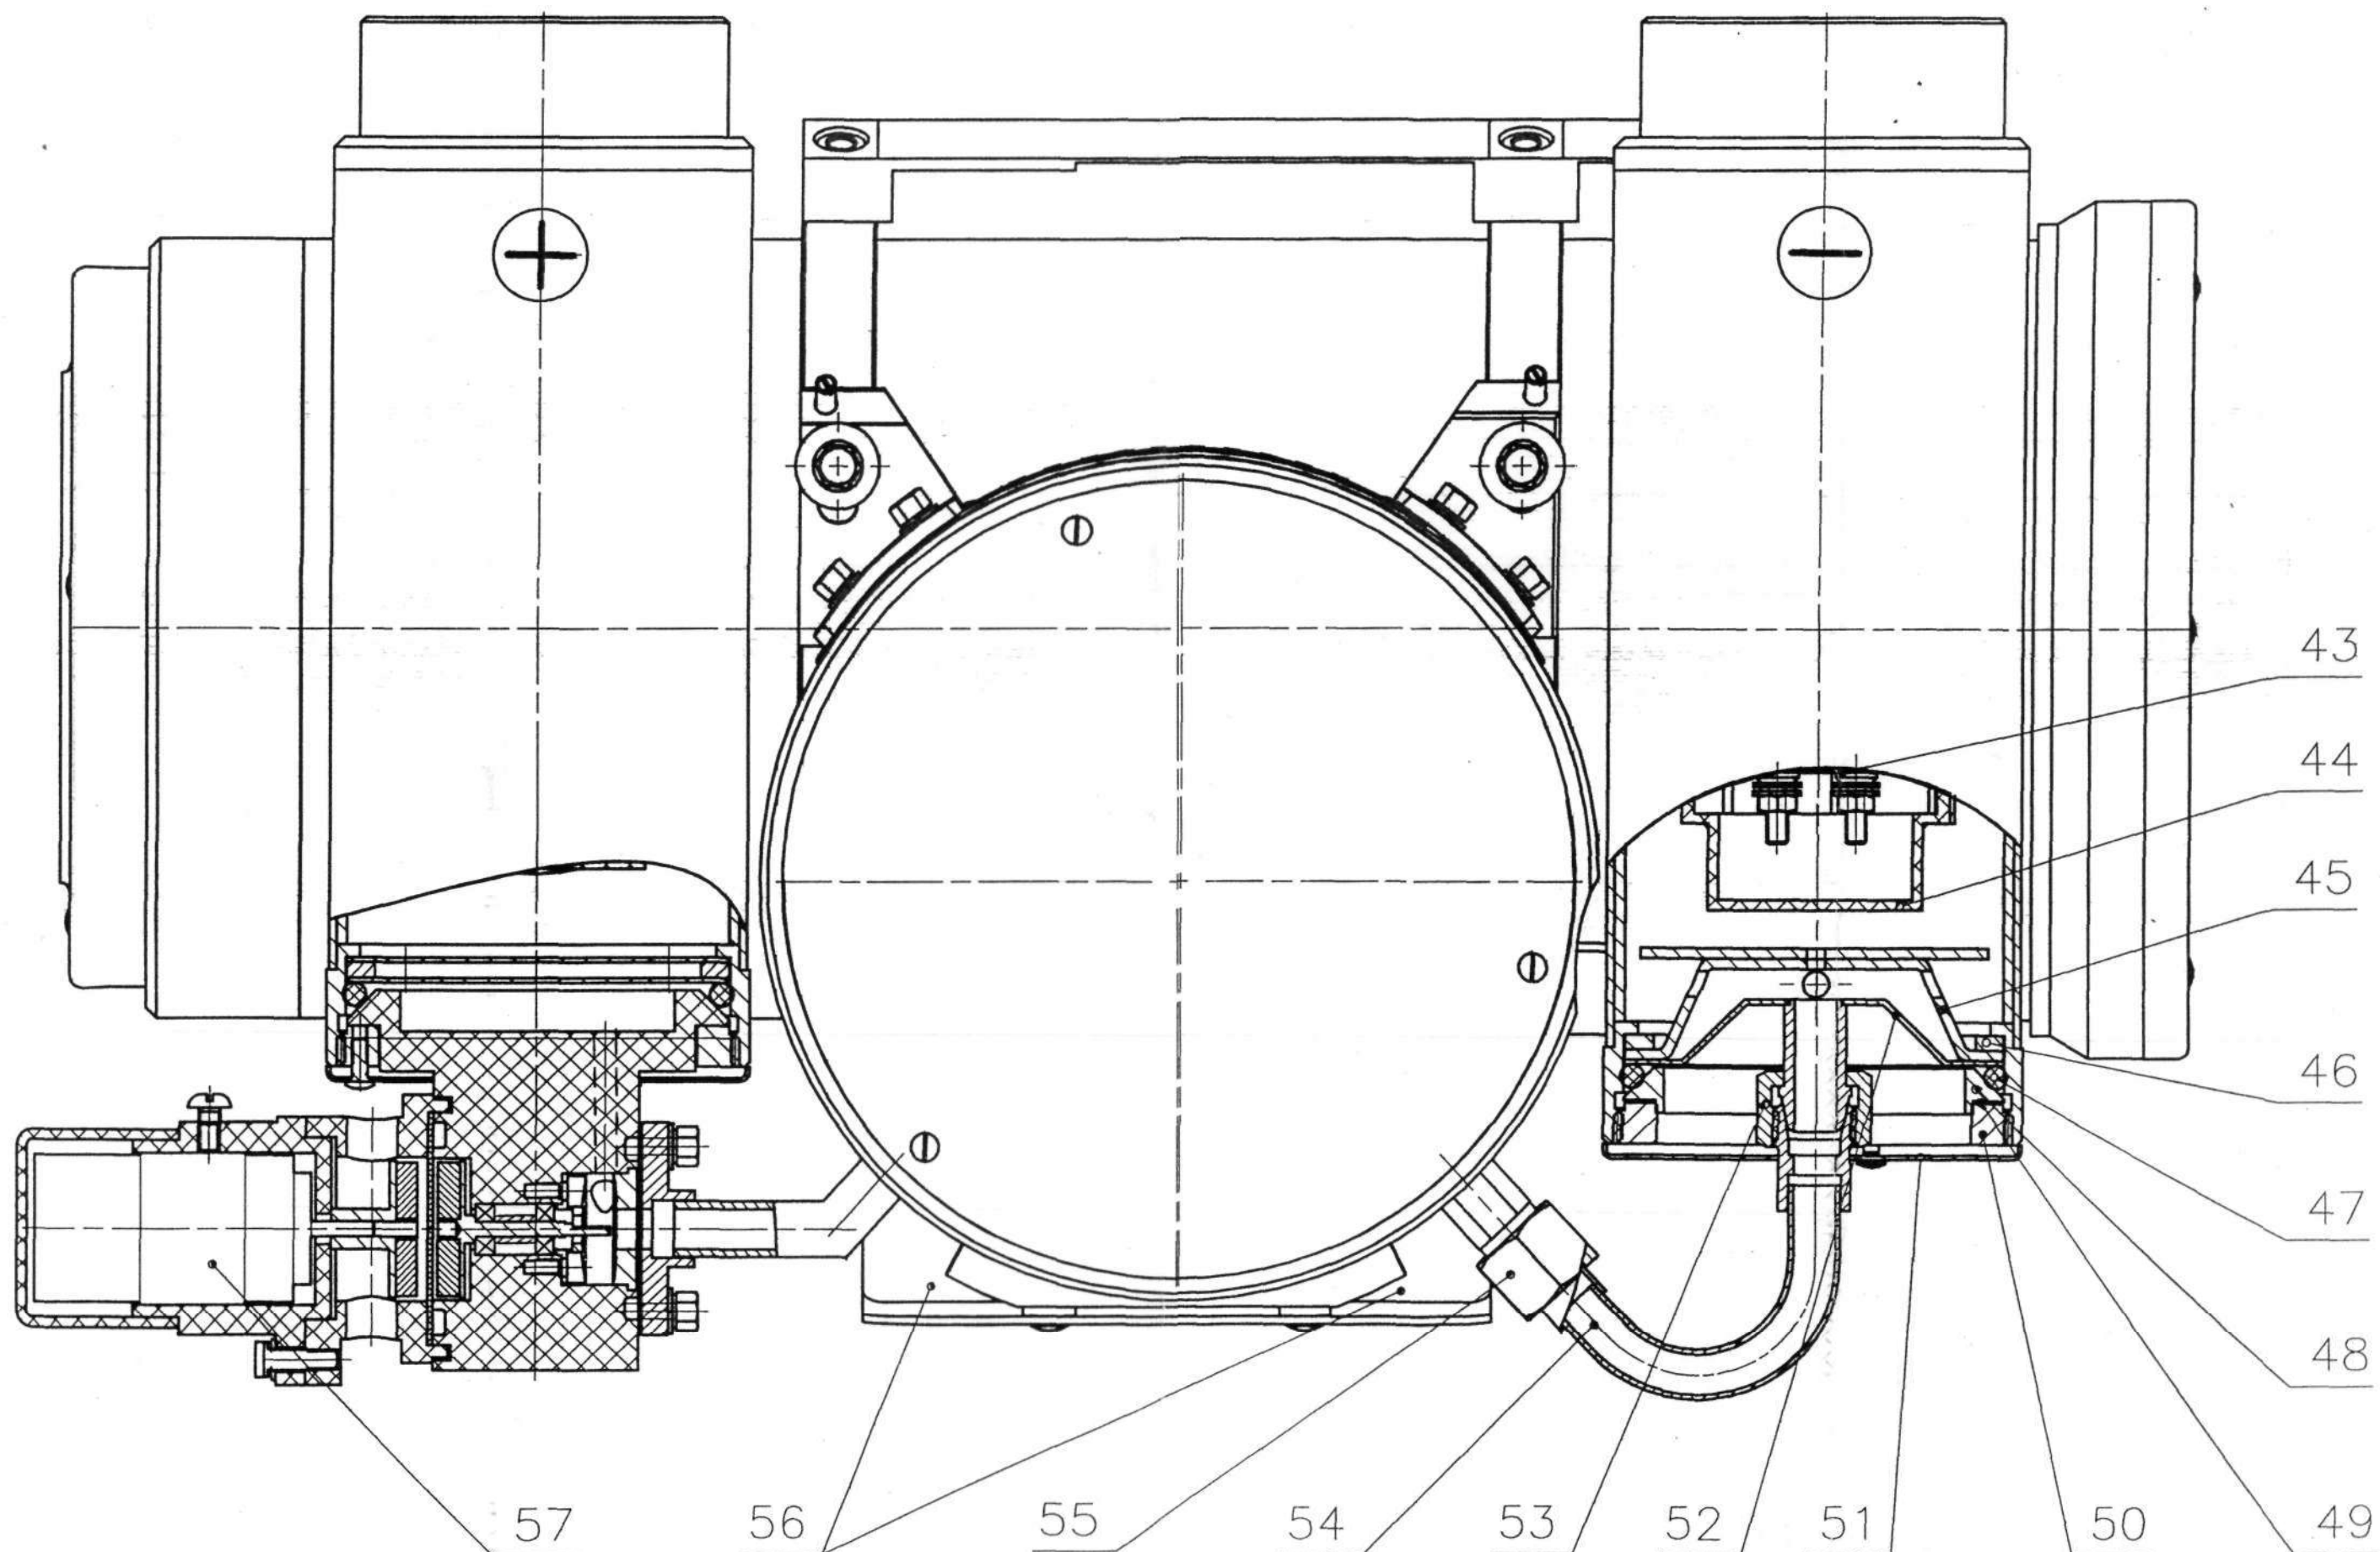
Излучатель рентгеновский, Вид А (см. рисунок 2)
